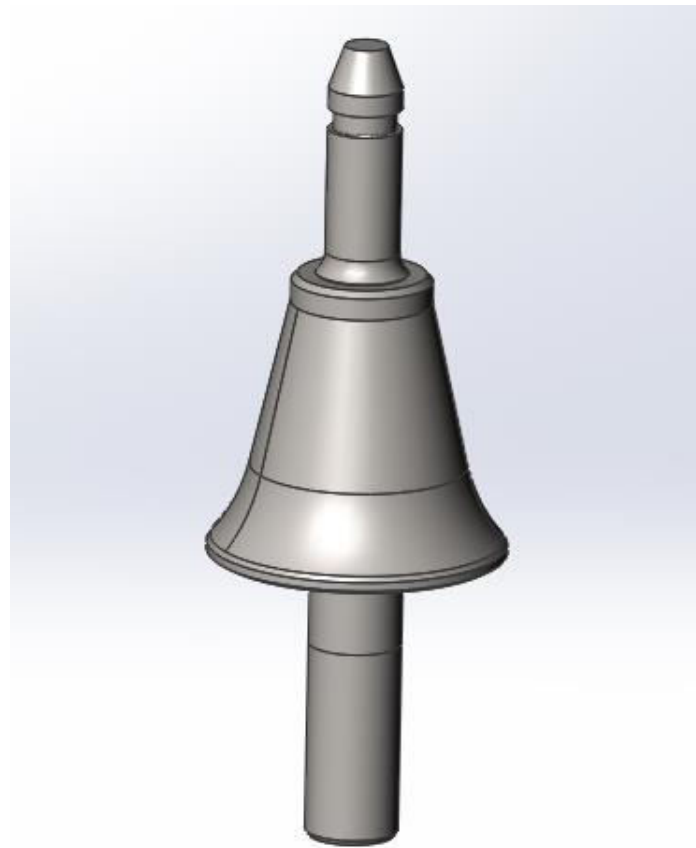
Комп'ютерна модель конуса дробарного дробарки конусної КРД 700-75
